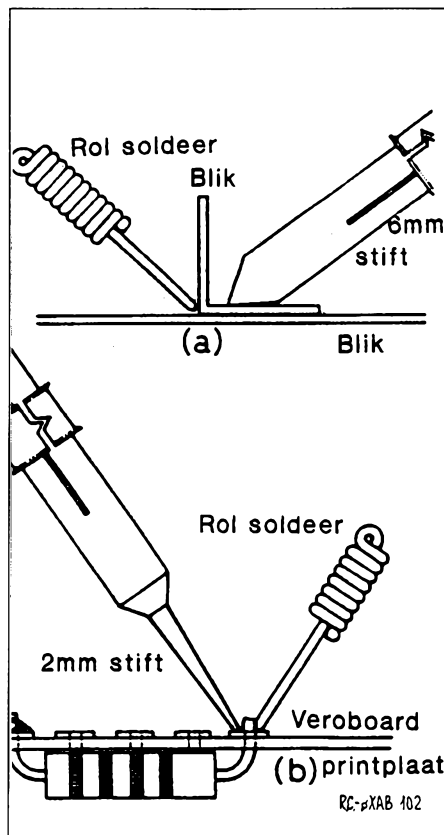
Gebruik een flinke soldeertip (a) voor het solderen van blik en een dunne stift (b) voor de componenten. Let op de handige vorm van de rol soldeer.
